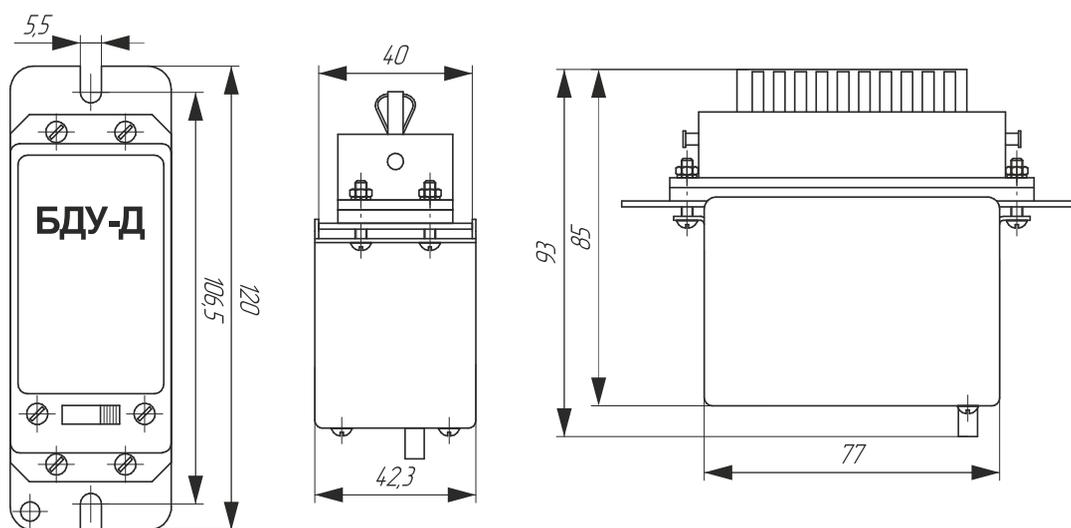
Габаритные и присоединительные размеры блока в исполнении БДУ-хД.1хх
